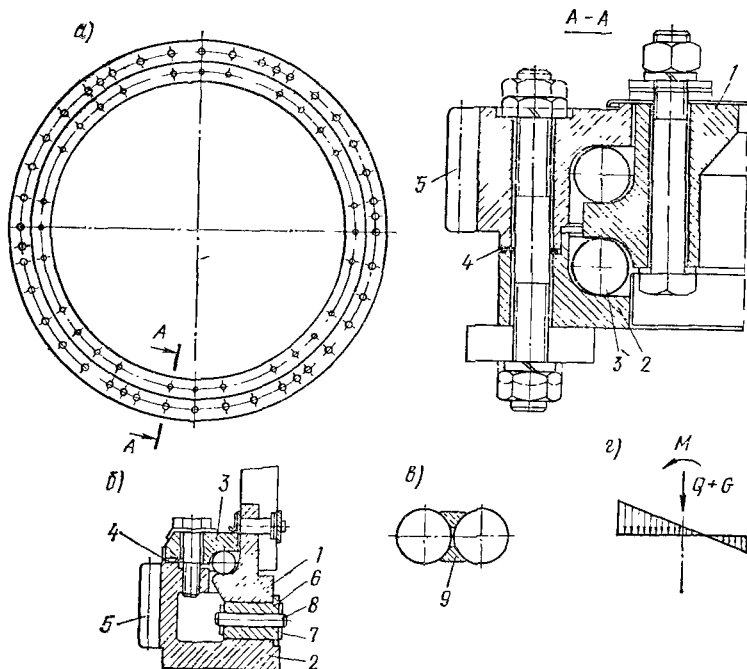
Опорно-поворотное устройство с осевыми телами качения (катками)
